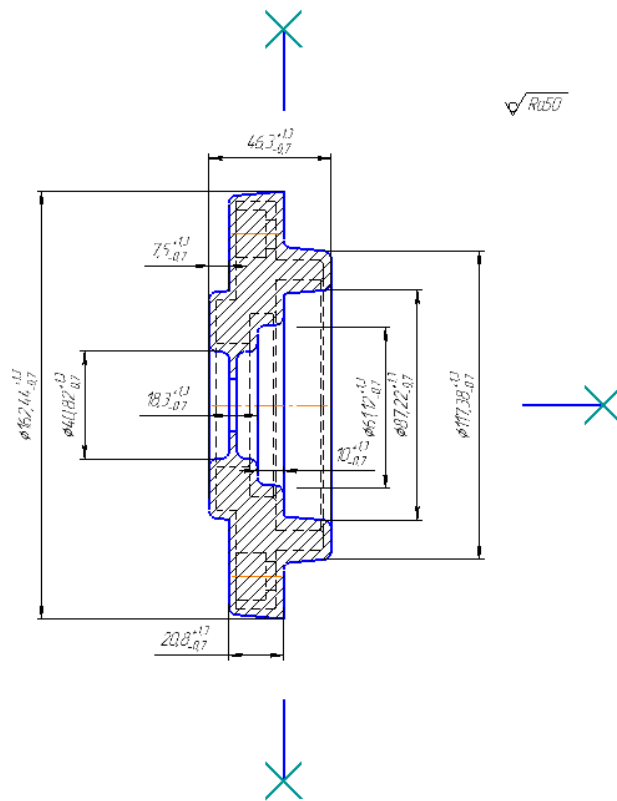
Ескіз заготовки, отриманої на ГKM
